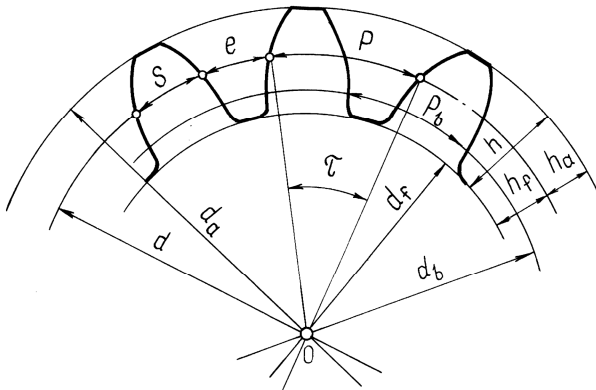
Цилиндрическое эвольвентное зубчатое колесо без смещения
